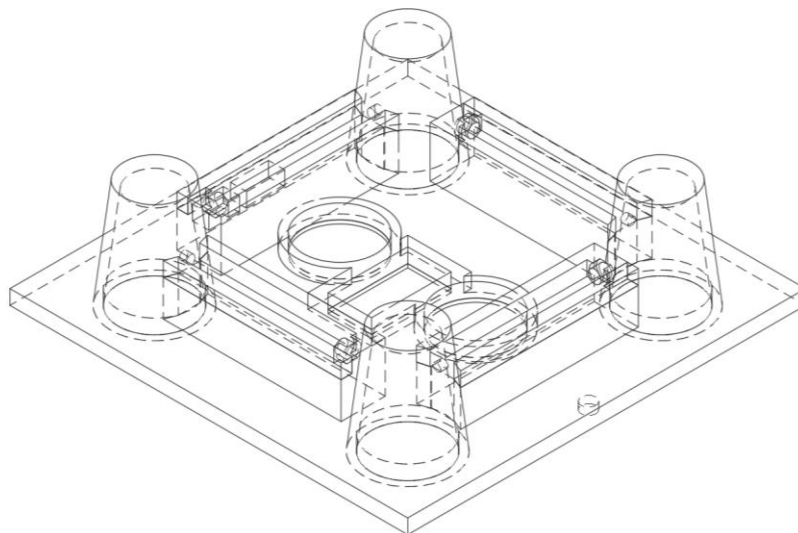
Корпус пристрою для швидкої заміни інструмента маніпулятора
